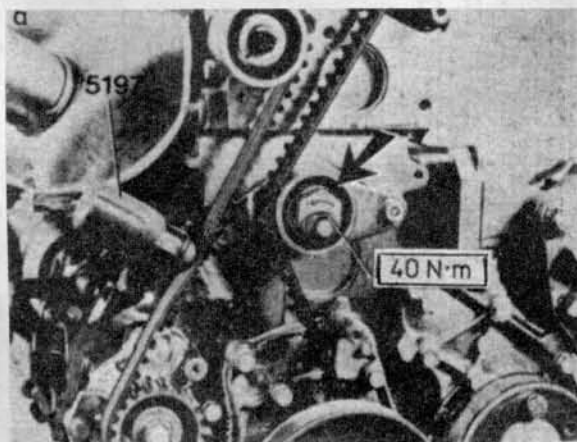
Измерение натяжения зубчатого ремня привода механизма газораспределения двигателя B172
